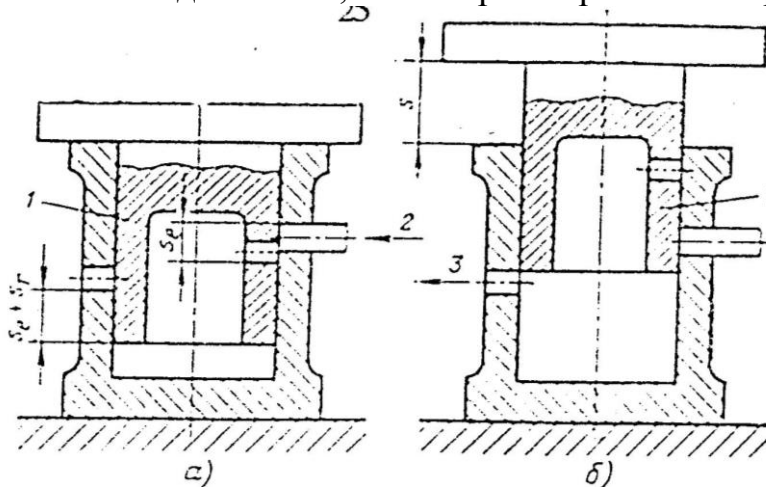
Схема установки струшу вальної машини на фундамент з пружним шаром
